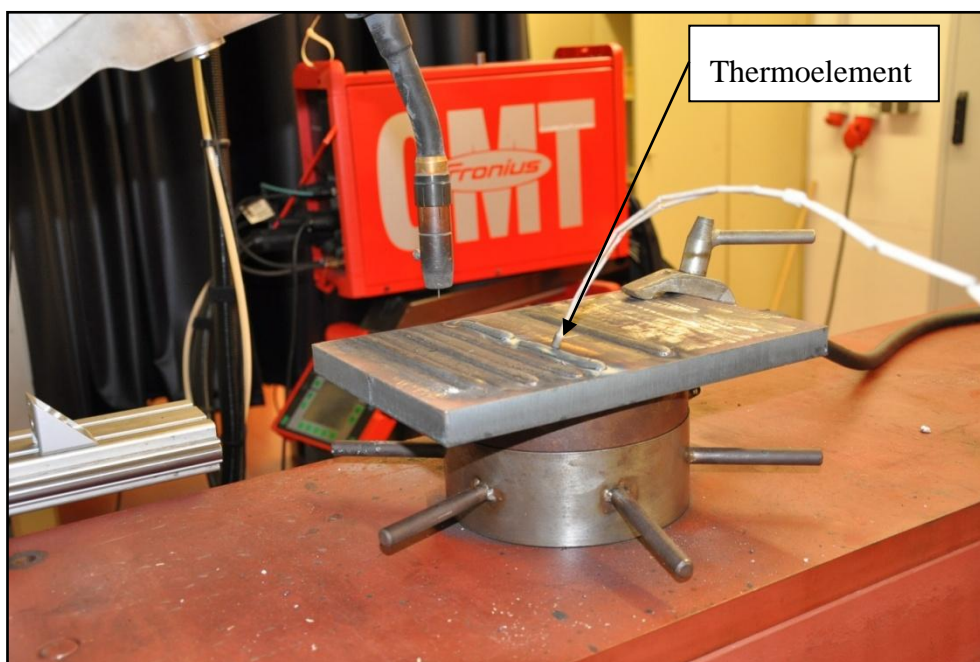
Eintauchversuch des Thermoelements in das Schweißbad
